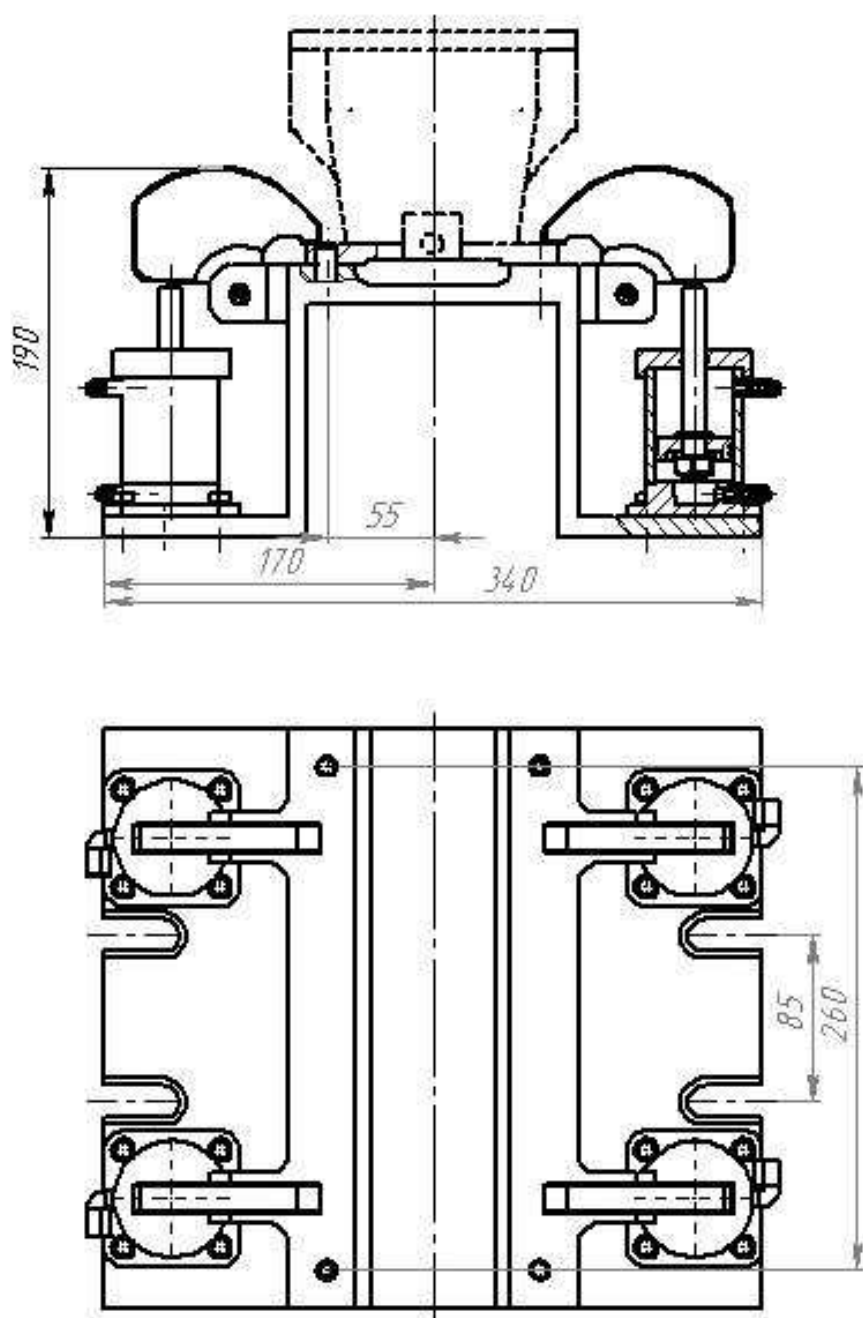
Схема приспособления для корпуса редуктора на операции 020 «Сверлильно-фрезерно-расточная
